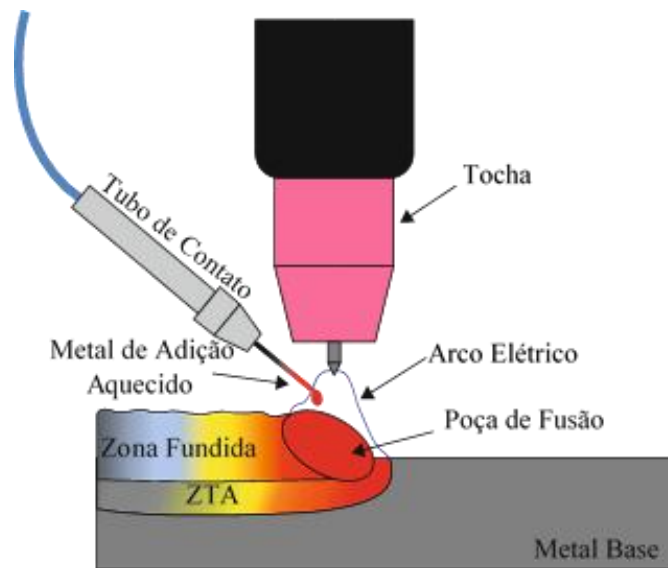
Representação esquemática do processo de soldagem GTAW arame quente (adaptado de [18]).
